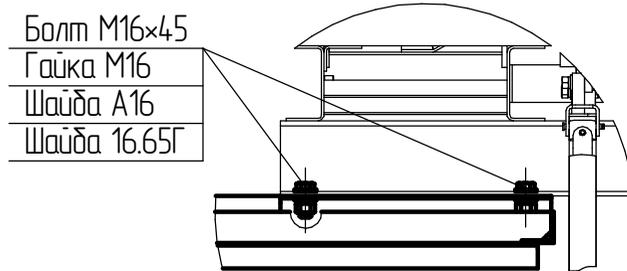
Установка на блок выключателя 35 кВ защитных сетчатых панелей над приводами разъединителя и выключателя
